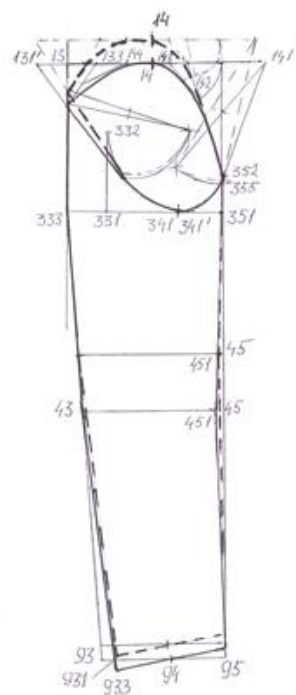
Чертёж базовой конструкции рукава платья для девочки младшего школьного возраста, размер 146-72-66
